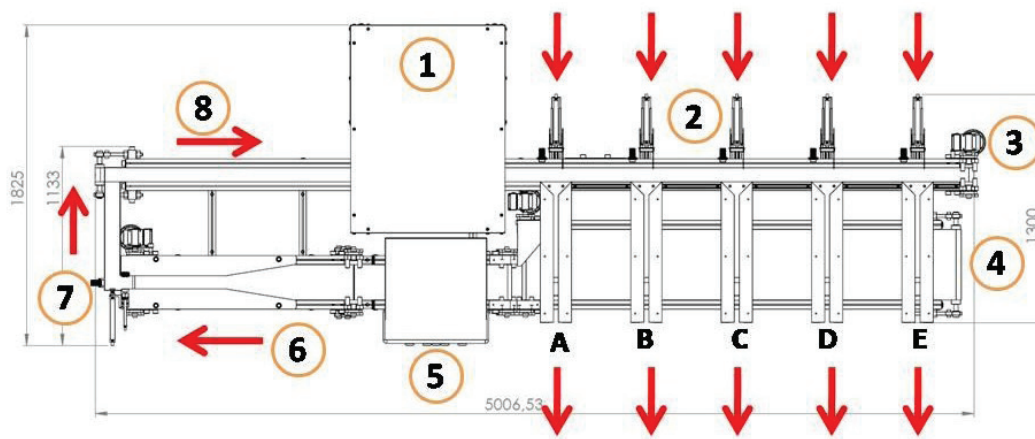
Vista de topo do layout de máquina proposto com destaque aos principais componentes funcionais do equipamento.
